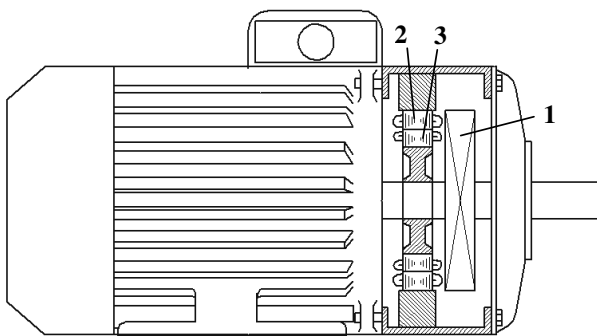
Размещение возбудителя в корпусе БСГ-250:
